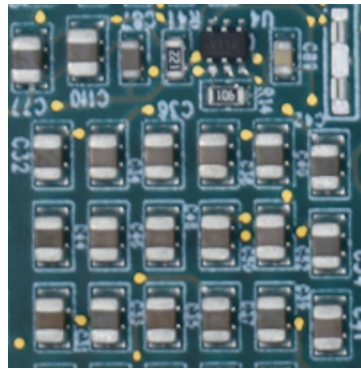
Componentes SMD soldados sobre el PCB
